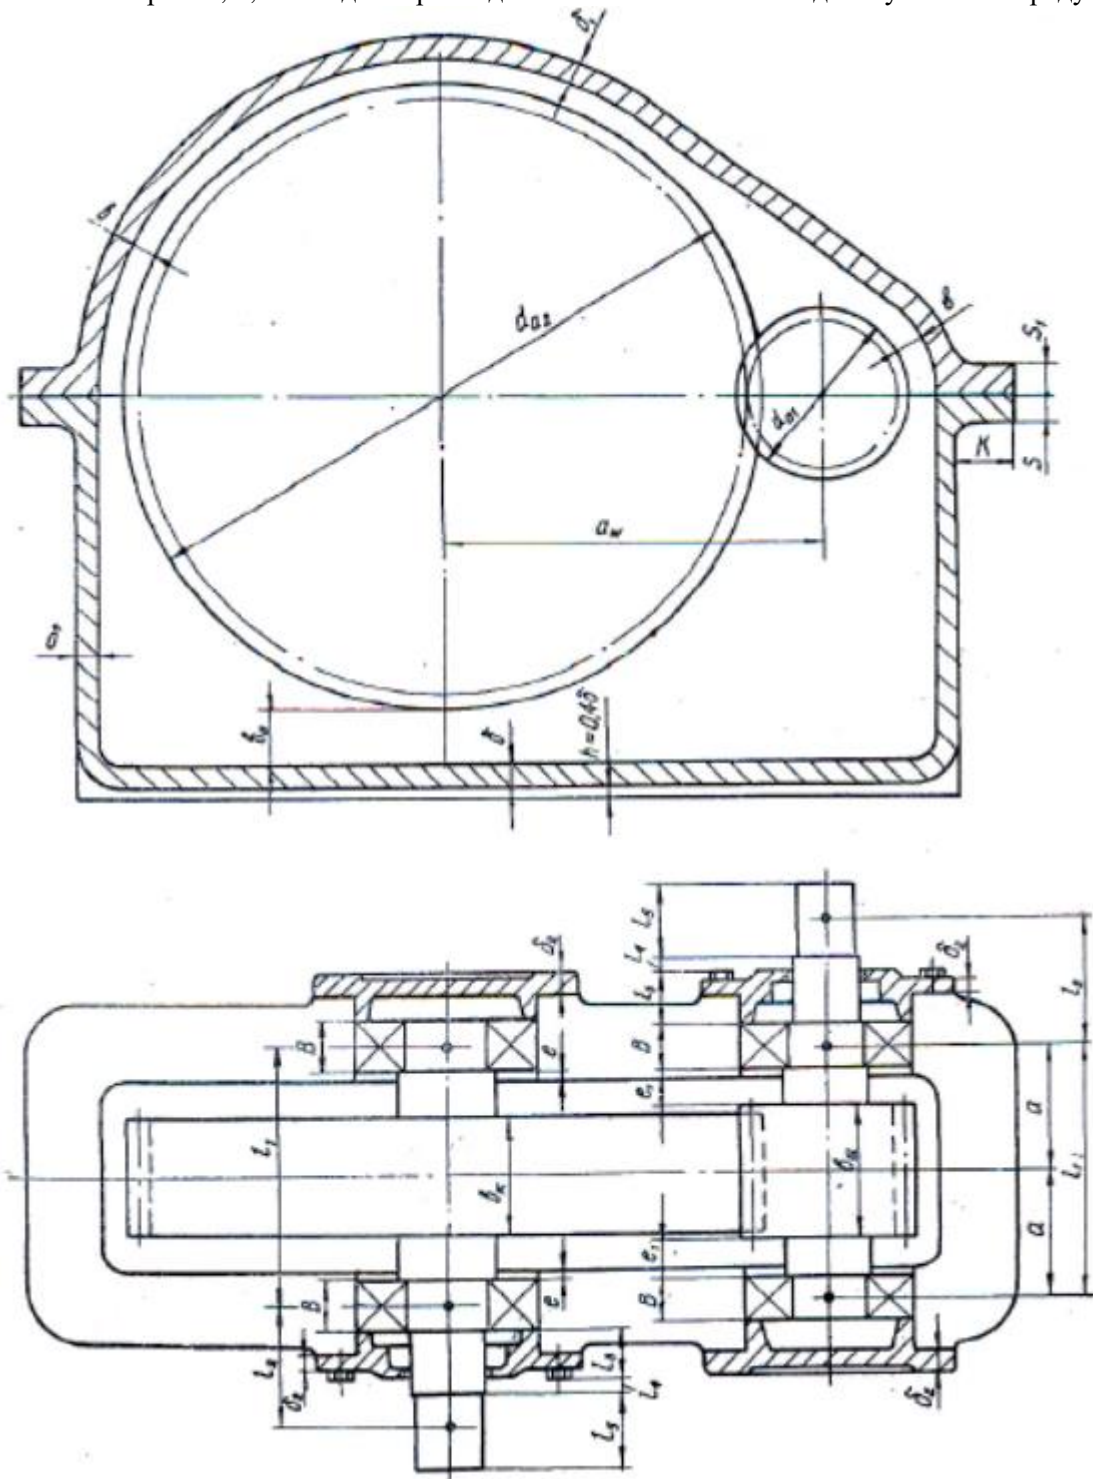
Ескізна компоновка одноступінчастого циліндричного редуктора
